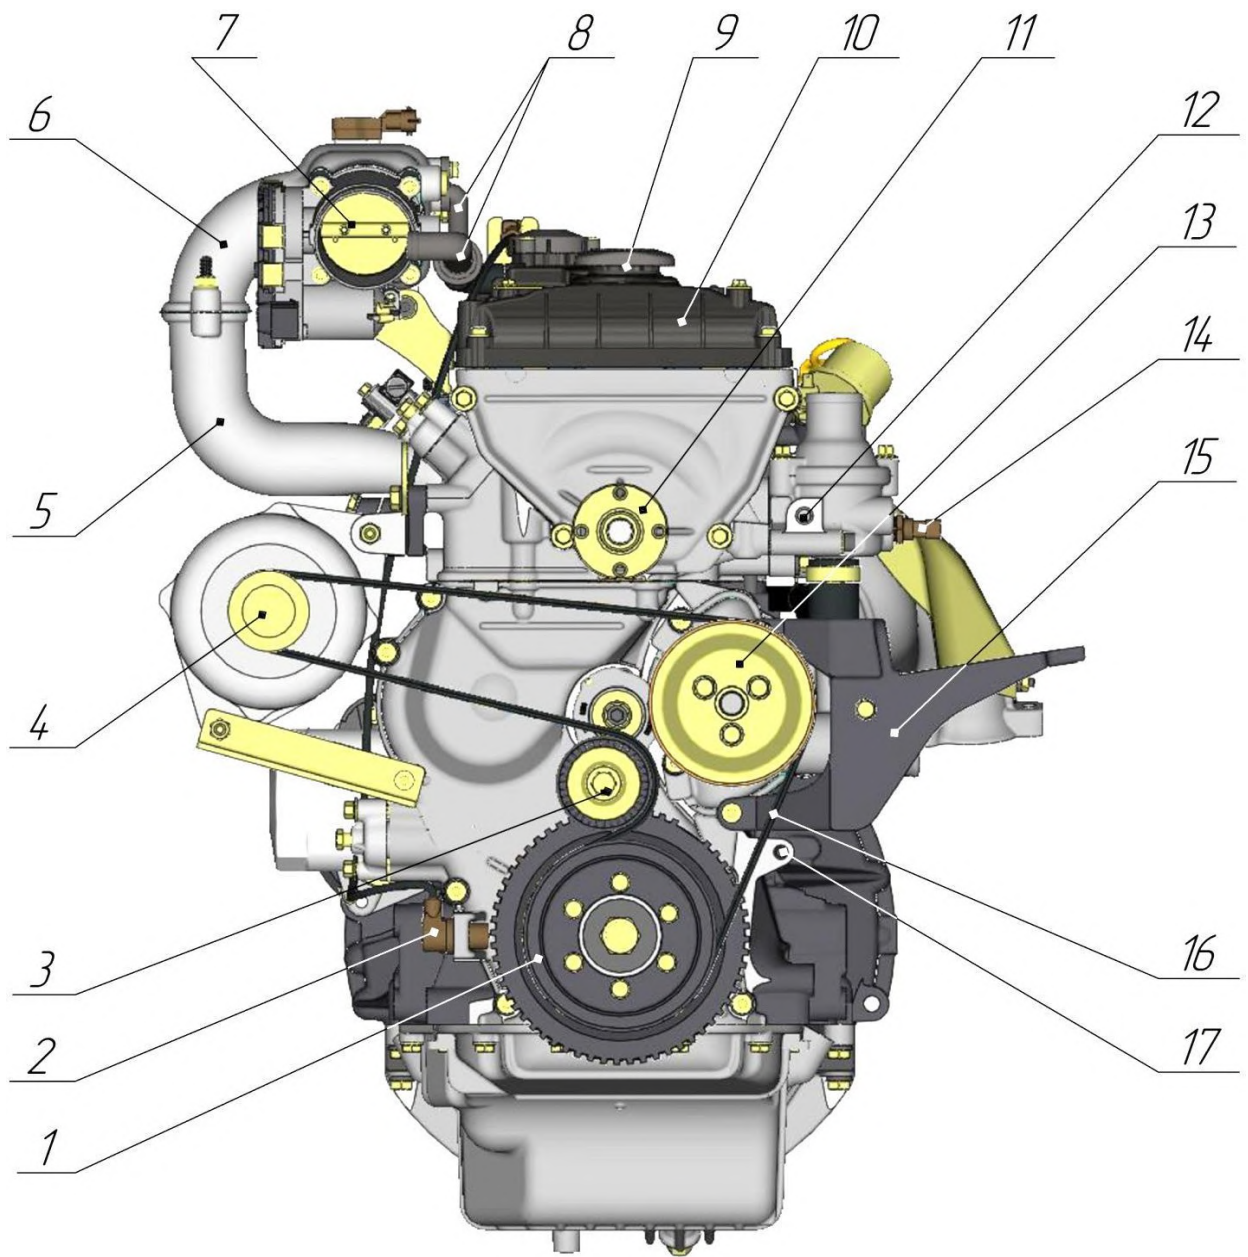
Vorderansicht des Motors ZMZ-40905.10:
